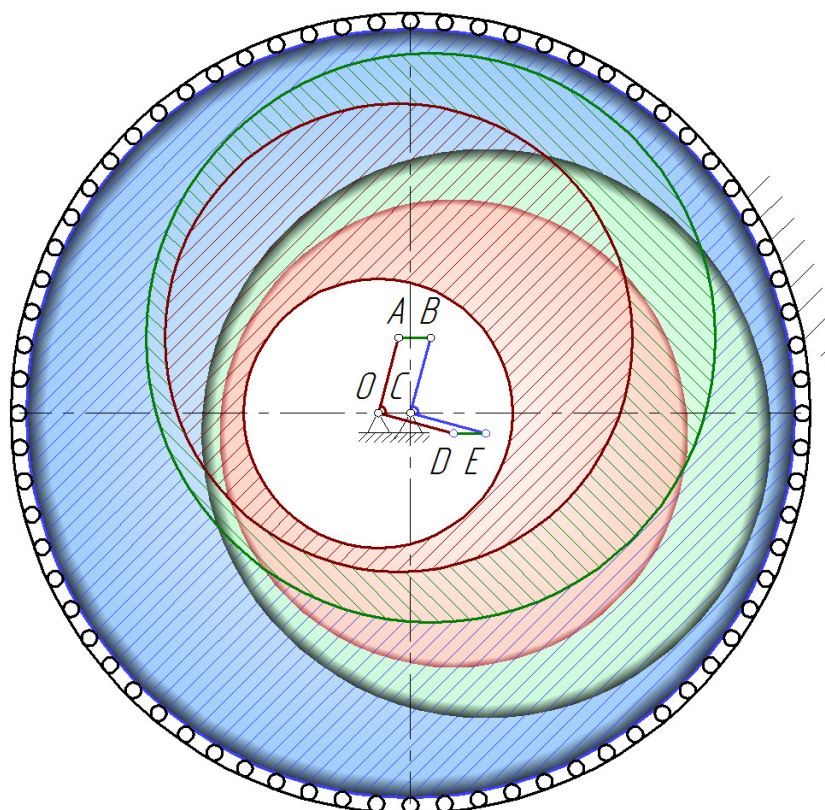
Схема трехъярусного подшипника с двумя шатунами
